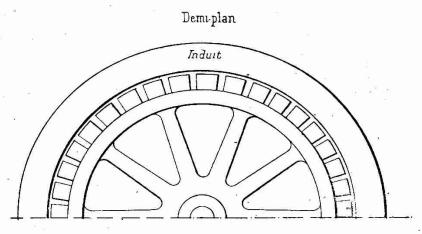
Alternateur vertical « à parapluie » Brown-Boveri. Vue en plan.
